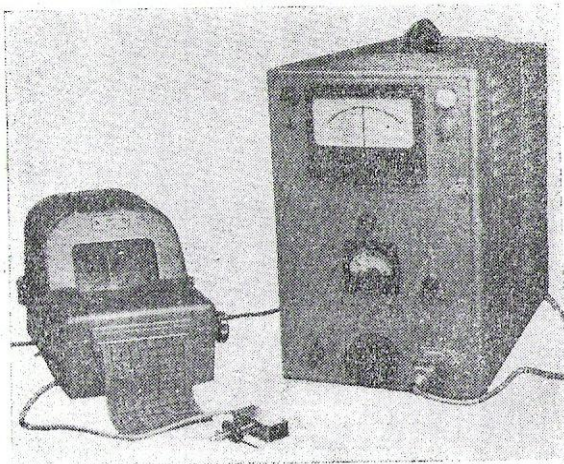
Индуктивный прибор модели 260 завода «Калибр»
